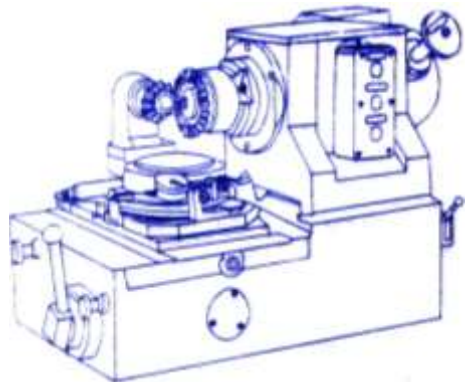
Автоматизированный прибор двухпрофильного контроля для конических зубчатых колес конструкции МПКТИ
